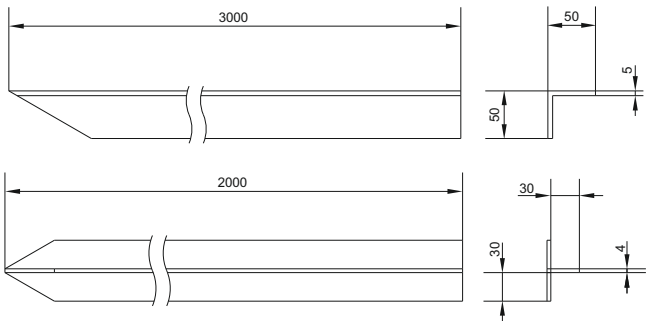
Габаритные размеры уголка / Figure 1 – Overall dimensions of the angle / 1 сурет – Бұрыштың жалпы өлшемдері
